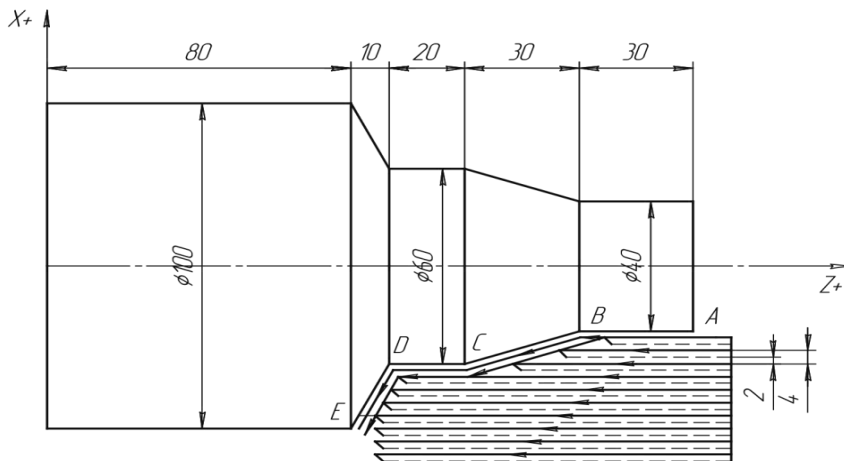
Чертеж вала и траектория движения резца по циклу чернового и чистового продольного точения
